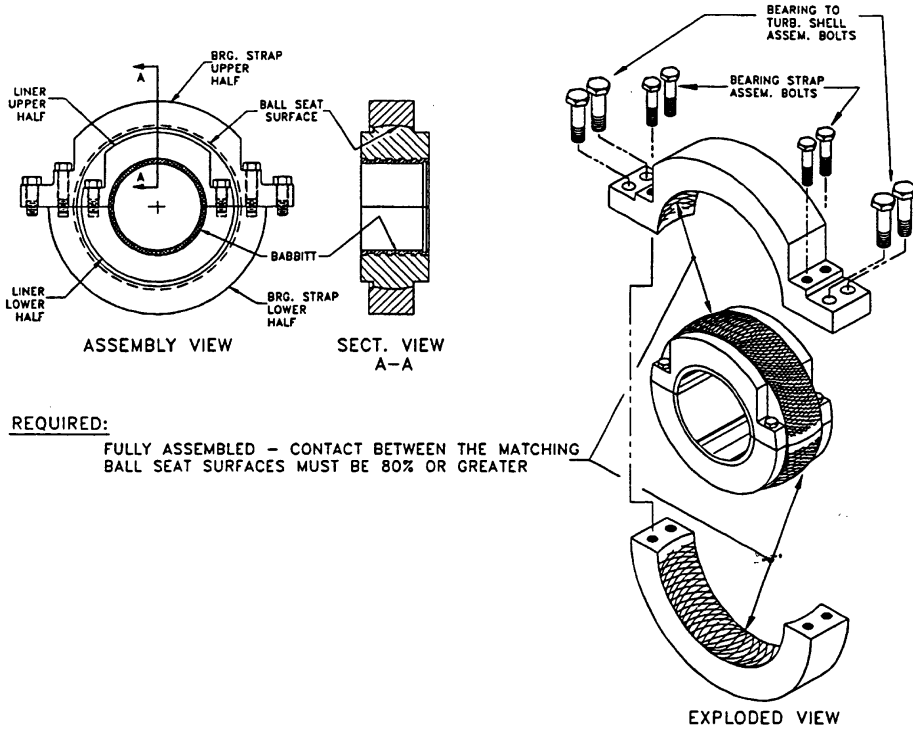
Ball Seat 저널 베어링의 Contact Check
